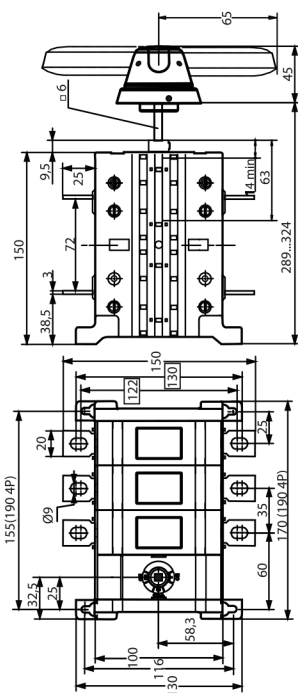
Габаритные и установочные размеры реверсивных рубильников 160-250А
